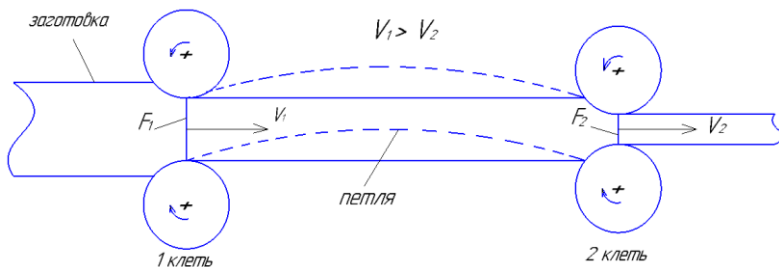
Схема одновременной прокатки заготовки в двух рабочих клетях
